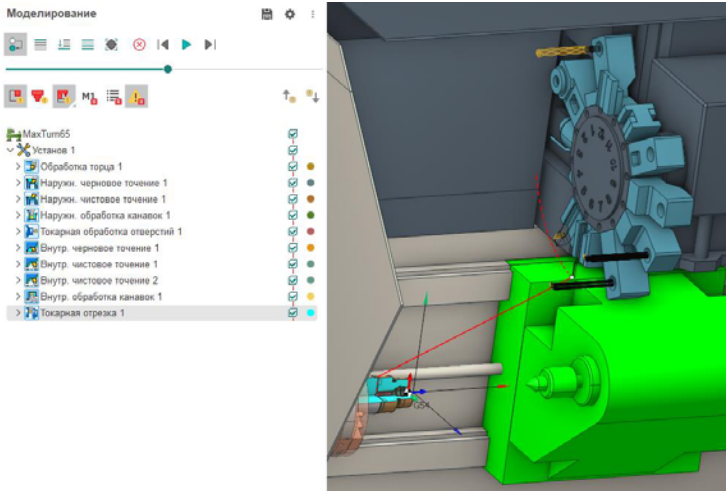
Расположение инструмента в револьверной головке станка.
